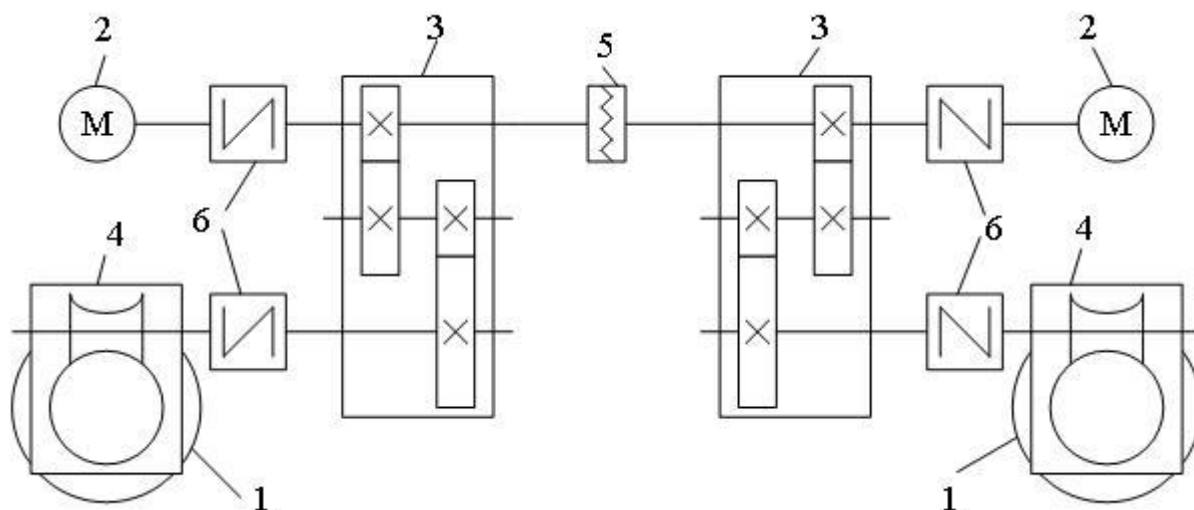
Кинематическая схема электропривода нажимных валков: 1 – нажимные винты; 2 – электродвигатель; 3 – цилиндрический редуктор; 4 – червячный редуктор; 5 – электромагнитная муфта; 6 – муфты
